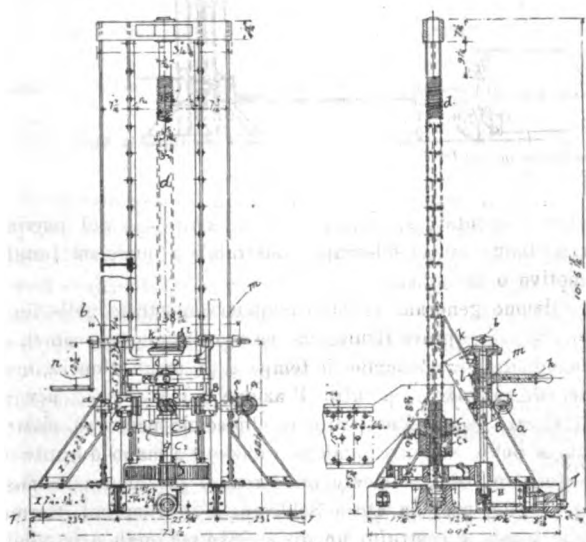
e 23. — Cavalletti Schlesinger - Elevazione e Sezione.
